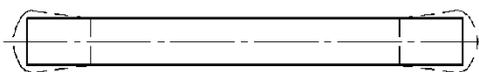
Уширение при прокатке полосовой заготовки переменной толщины
